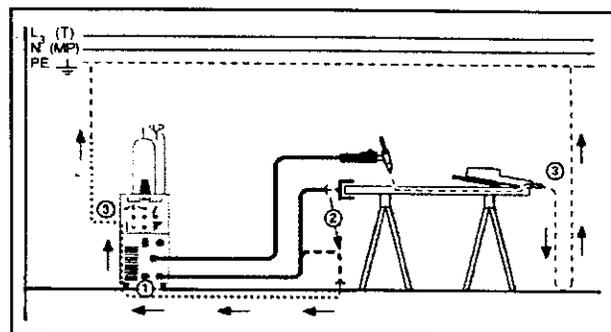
① Nunca posicione a máquina de solda sobre uma superfície condutora!
